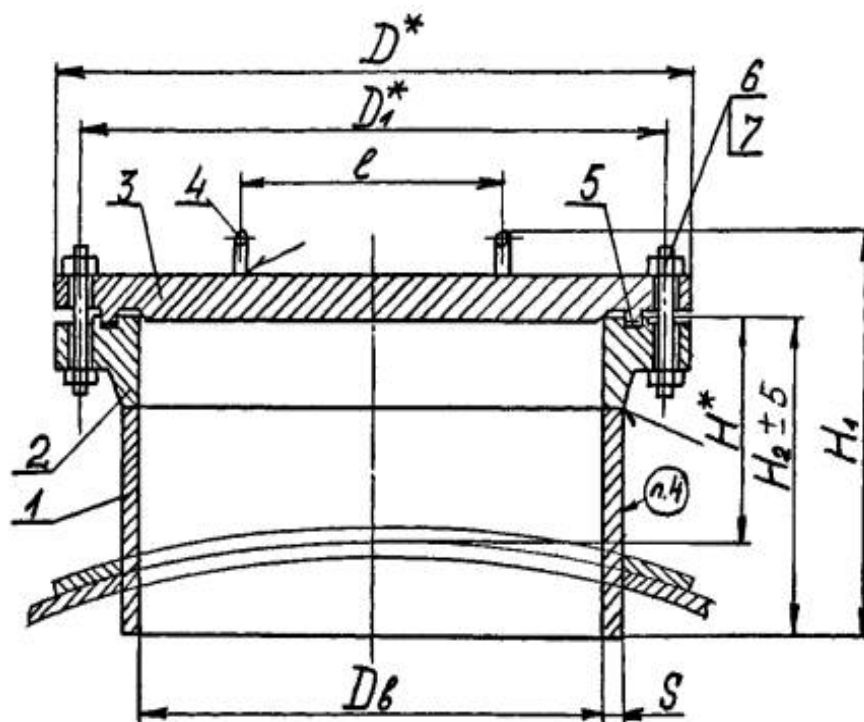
Рисунок люк-лак с уплотнительной поверхностью шип-паз с конструктивными размерами.
